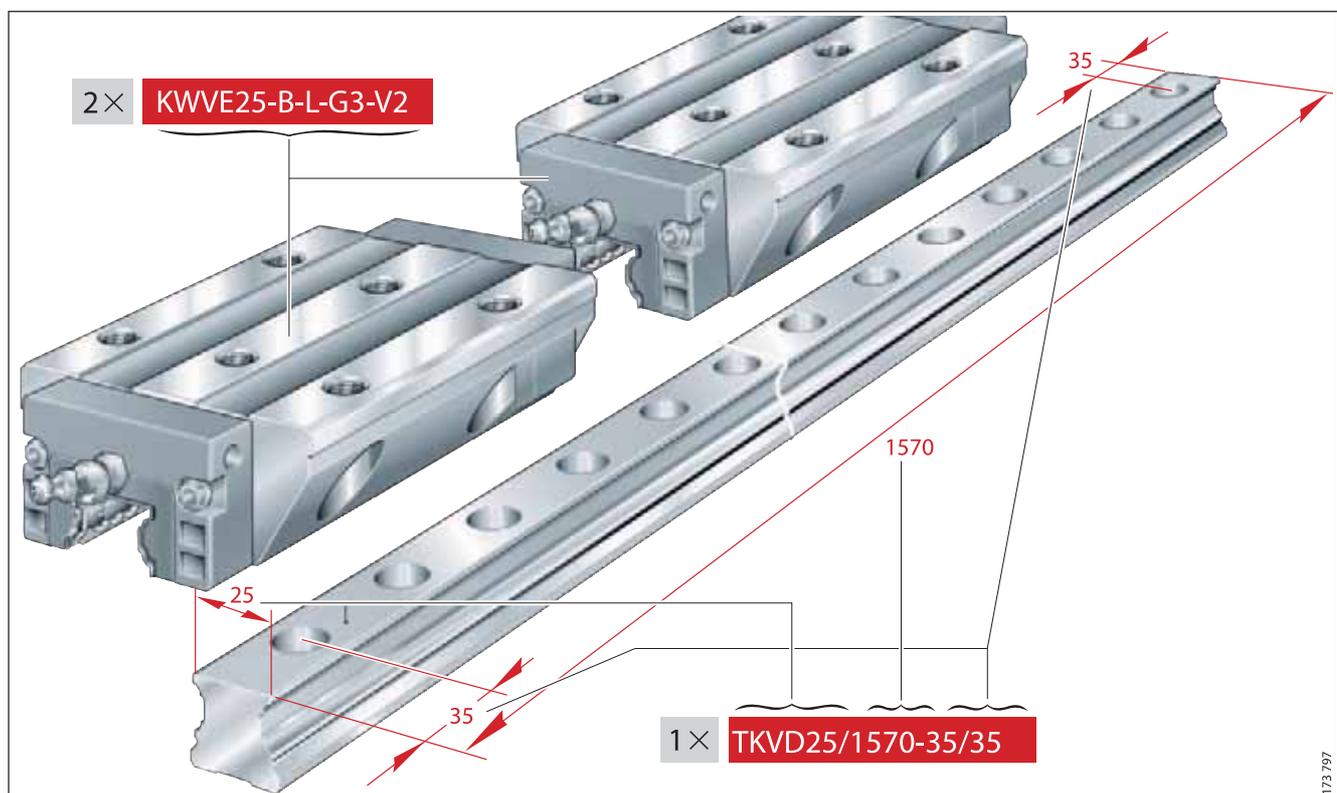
· Пример кареток и рельсов с обозначением для заказа
